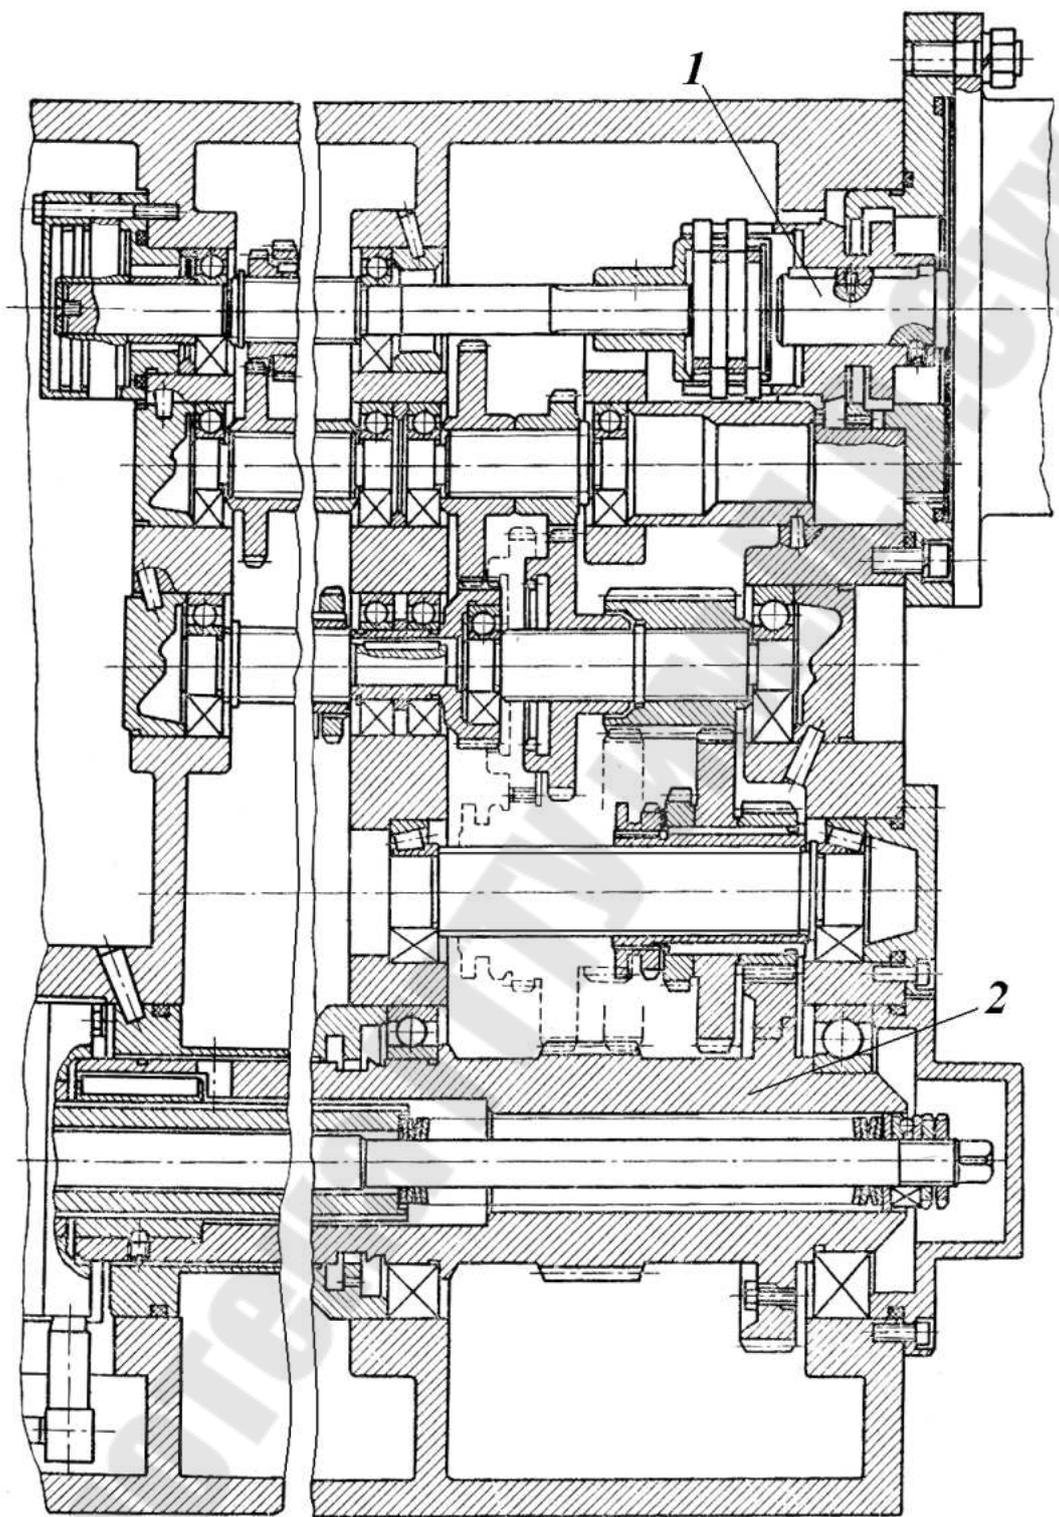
Коробка скоростей копировально-фрезерного станка 6Б443Г:
